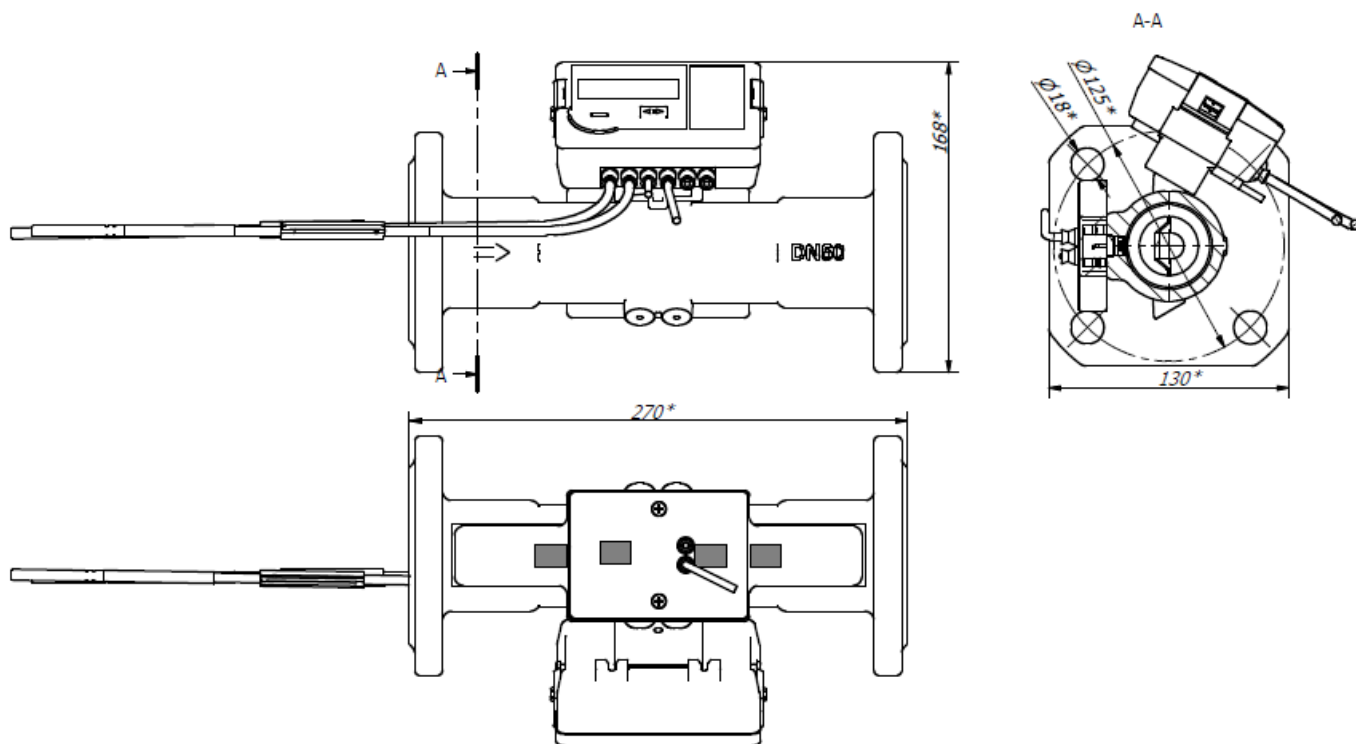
Присоединительный размер к трубопроводу DN50 , длина L= 270 мм
